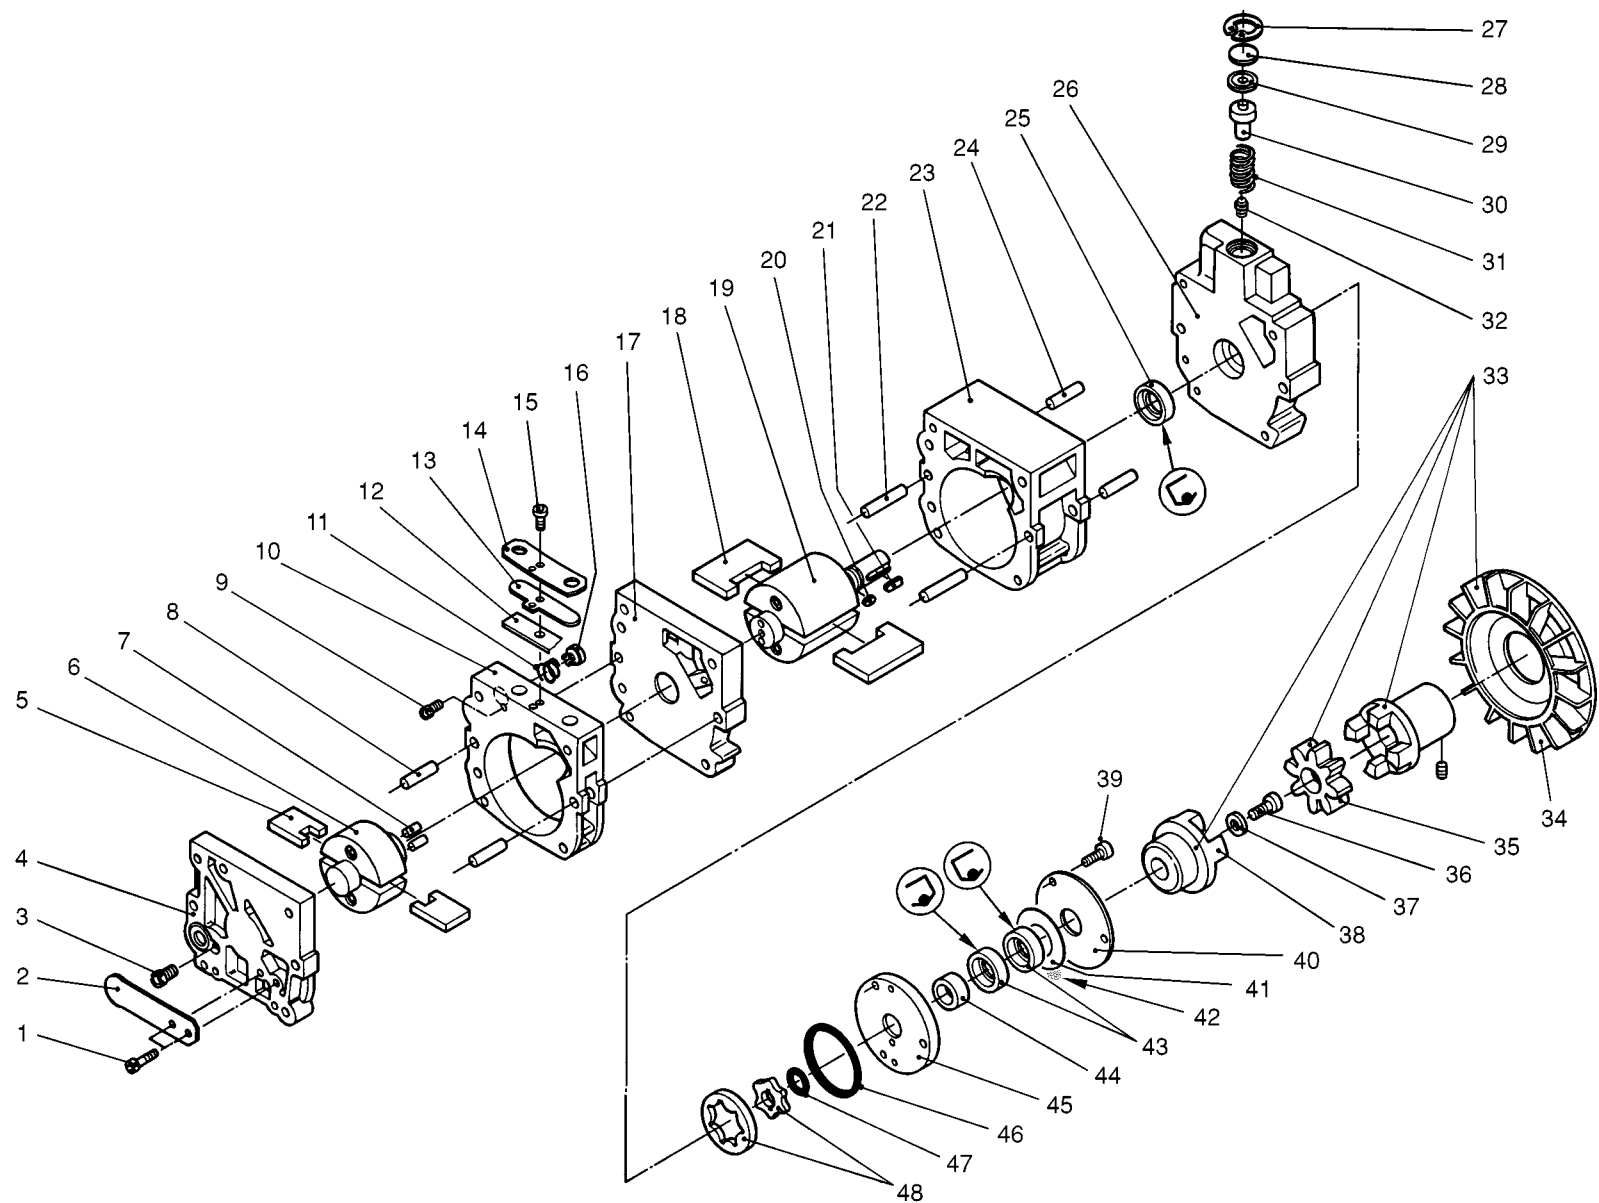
TRIVAC D 16/25 BCS-(PFPE) Innenteil / Pumping module / Corps de pompe
